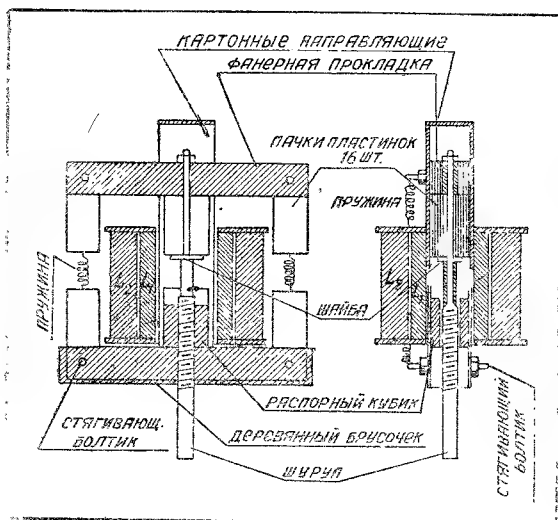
Сборочный чертеж выдвижного сердечника и катушек
